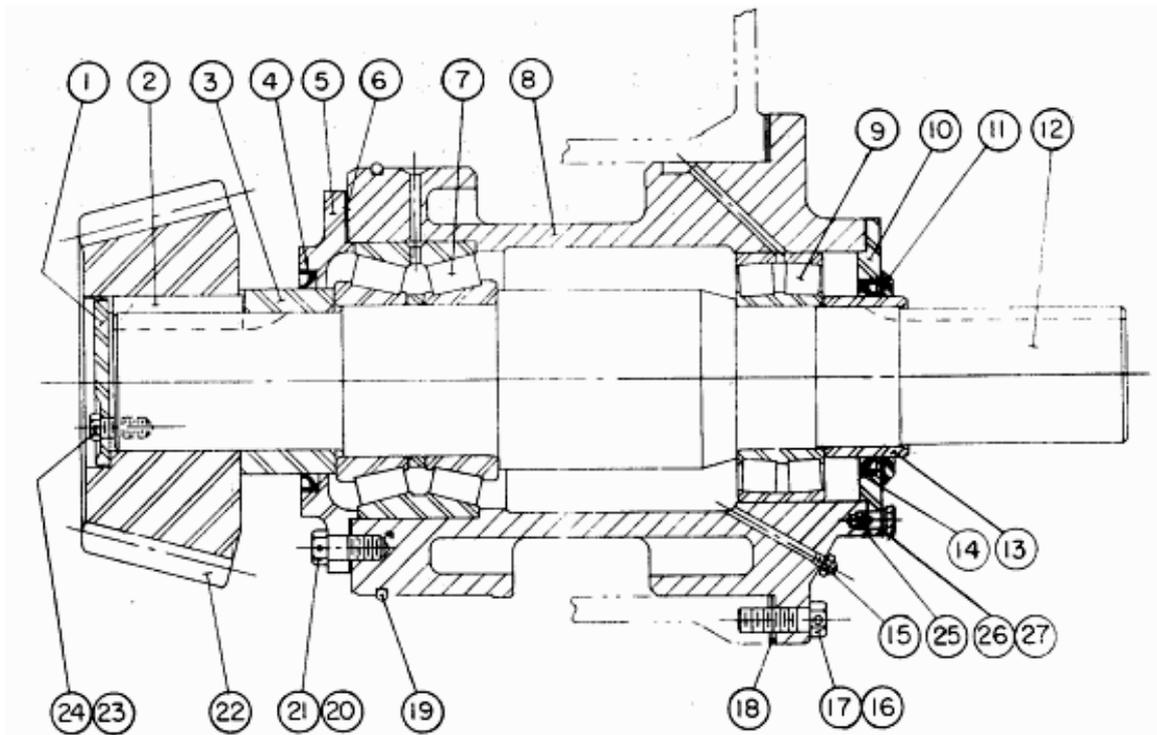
Dessin en coupe d'un montage arbre pignon.[3]
